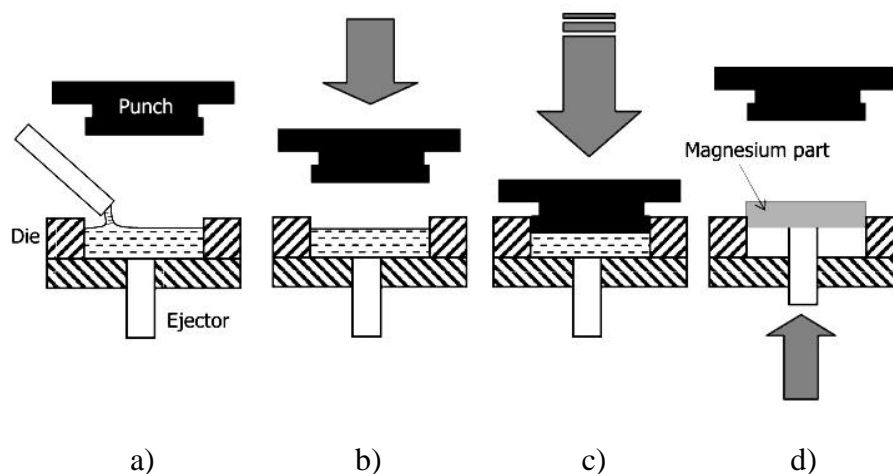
Nepřímá metoda squeeze castingu [8]
